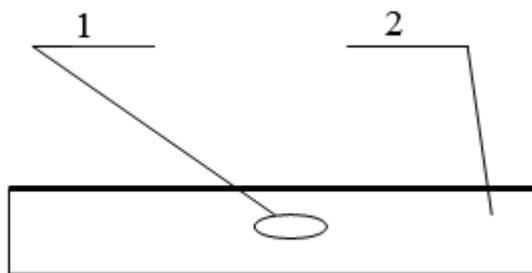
Конструкция контрольного сварного соединения
